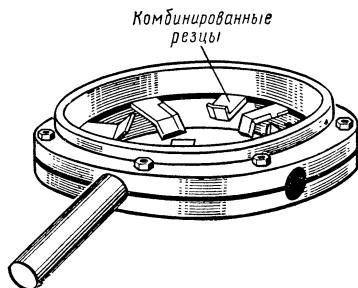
Фреза для обработки торцов полиэтиленовых труб перед сваркой
